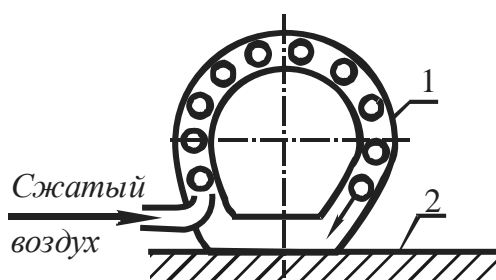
Схема портативного пневматического устройства: 1 – портативное пневматическое устройство, 2 – деталь
